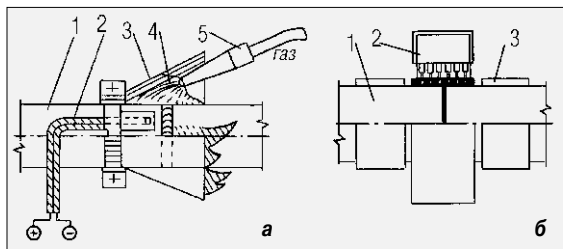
Газопламенный нагрев при термообработке сварных соединений трубопроводов: а — универсальной ацетилено-кислородной горелкой (1 — сварное соединение; 2 — термoeлектрический преобразователь; 3 — теплоизоляционная воронка; 4 — факел пламени горелки; 5 — универсальная ацетилено-кислородная горелка); б — кольцевой многопламенной горелкой (1 — сварное соединение; 2 — корпус кольцевой многопламенной горелки; 3 — теплоизоляция)
